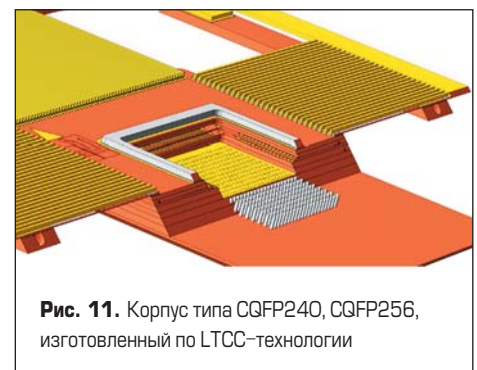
Корпус типа CQFP240, CQFP256, изготовленный по LTCC-технологии
